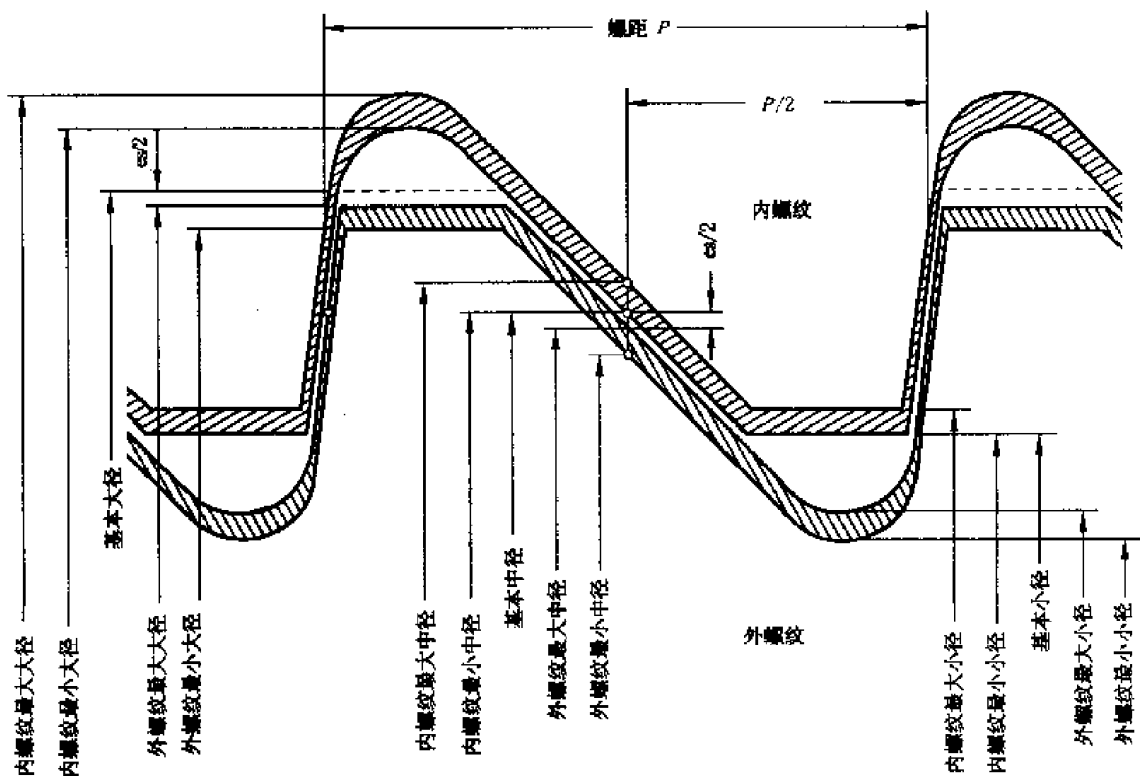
美制锯齿形螺纹的公差带位置
